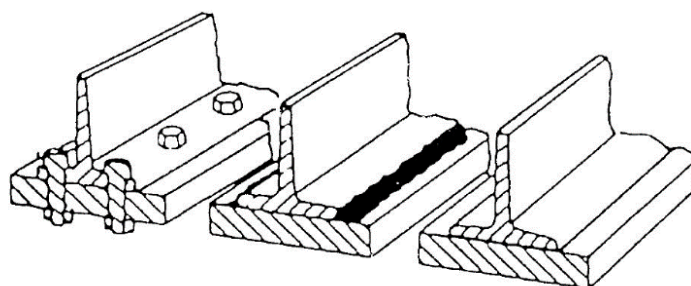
Ligação aparafusada, soldada e adesiva [2].
